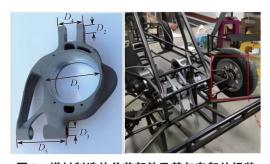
增材制造的关节部件及其与车架的组装 Fig. 9 Additively manufactured articulated parts and their assembly to the frame
